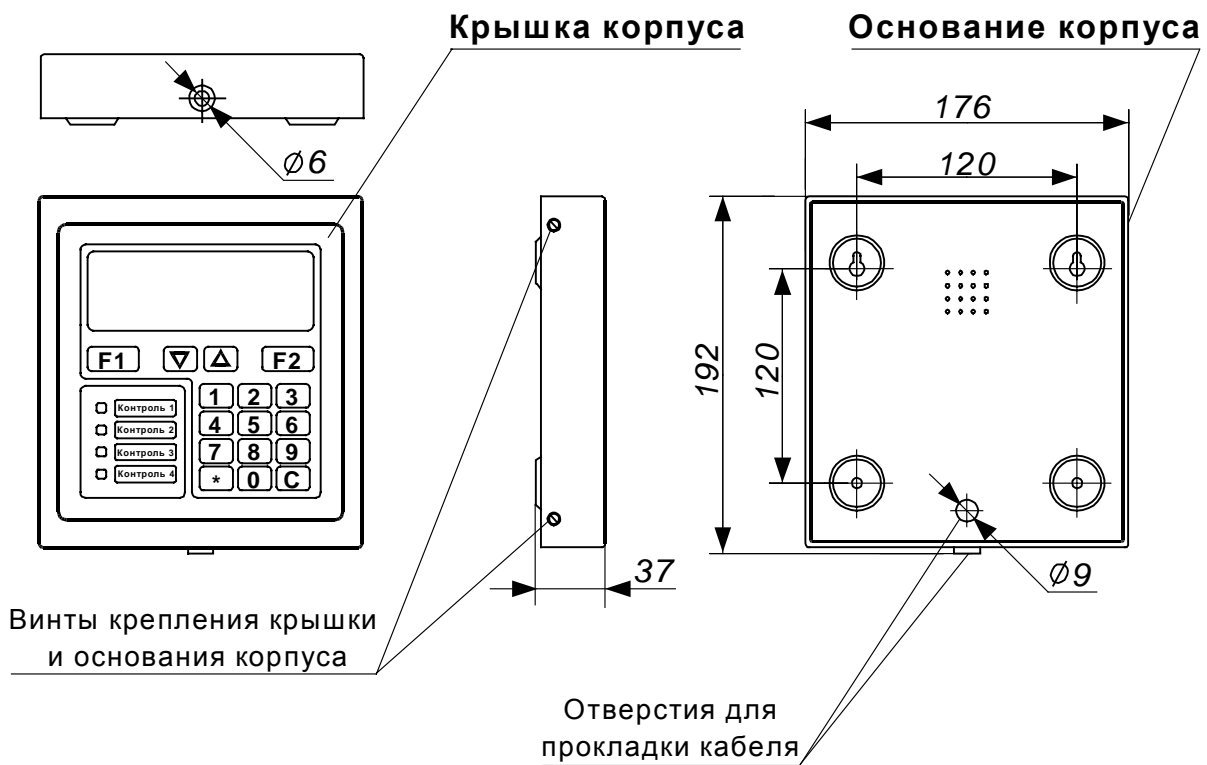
Габаритные и присоединительные размеры (накладное исполнение)
